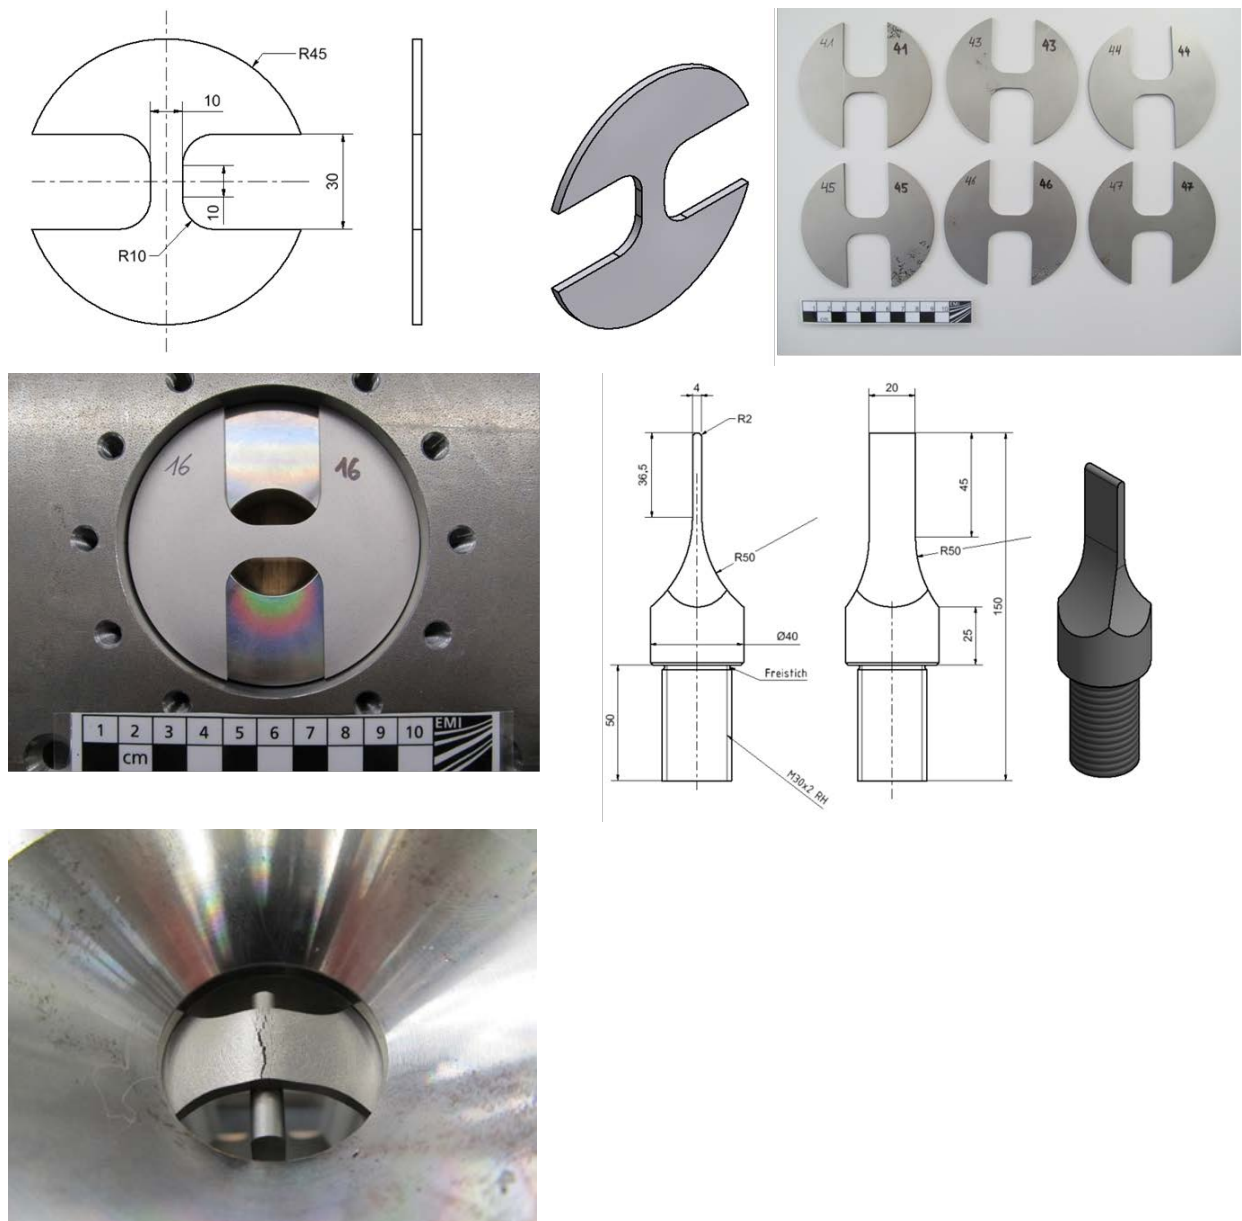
Zug-Biegeversuch: Proben, Werkzeuge, Einbau in VHS-Prüfmaschine
